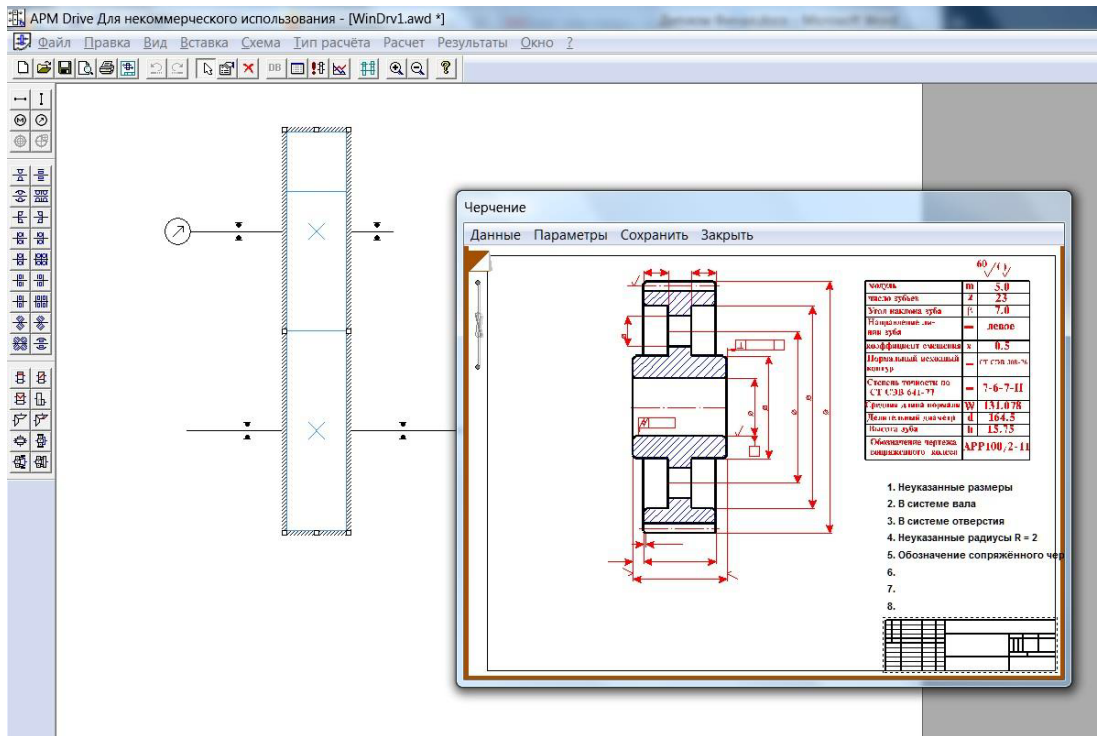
Зарисовка шестерни редуктора на ведомом валу
